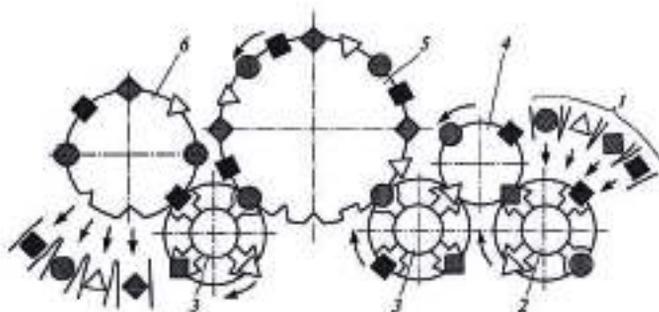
Схема многономенклатурной АРЛ для параллельной обработки деталей: 1 – заготовки; 2 – загрузочный ротор; 3 – транспортные роторы; 4 – контрольный ротор; 5, 6 – технологические роторы
